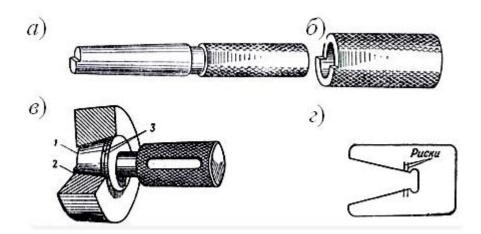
Общий вид конусных калибров: пробка и втулка с уступами (a, δ) , пробка с рисками и уступами (s), угловая скоба с рисками (z)
